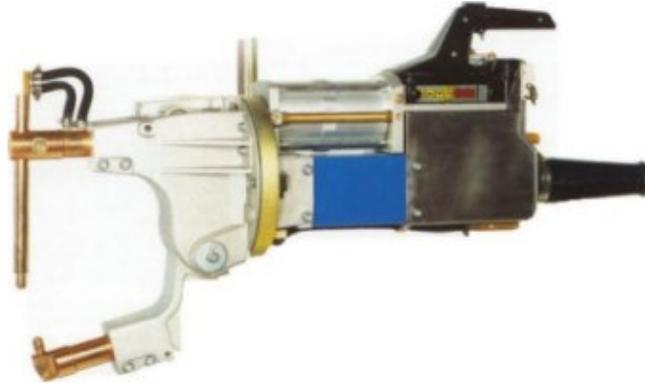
Maquinaria empleada para realizar el proceso de soldadura por resistencia (www.dextra.com).
